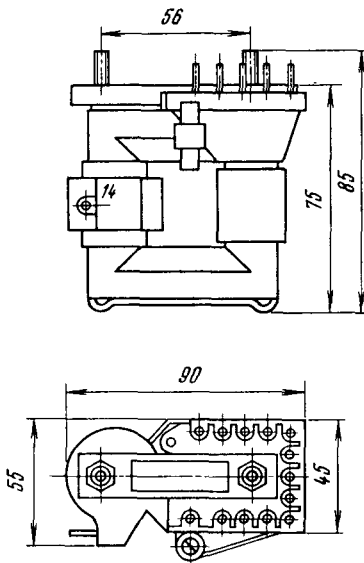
Общий вид трансформаторов строчной развертки типа ТВС-110ПЗ
